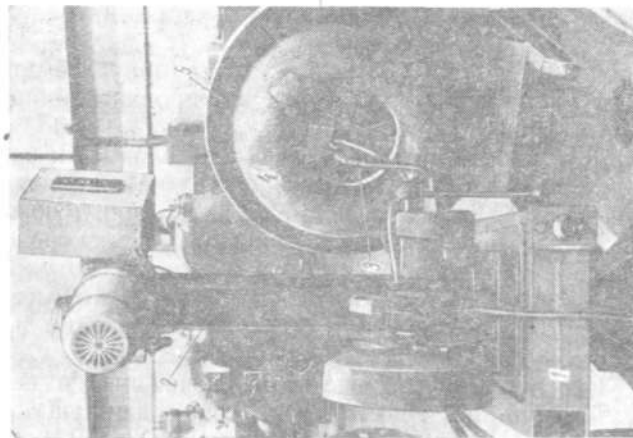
Установка для сварки кольцевых внутренних и наружных швов.
